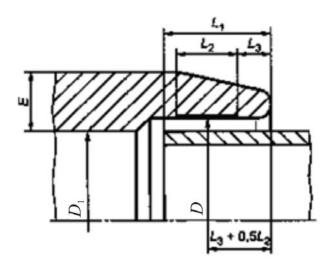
Размеры раструбных концов деталей: D — средний внутренний диаметр раструбного конца детали в зоне сварки;  $D_1$  — проходное сечение;  $L_1$  — расчетная глубина захода трубы или охватываемого конца детали с трубным концом;  $L_2$  — номинальная длина зоны сварки, соответствующая длине зоны нагрева;  $L_3$  — номинальная длина холодной зоны на входе детали
